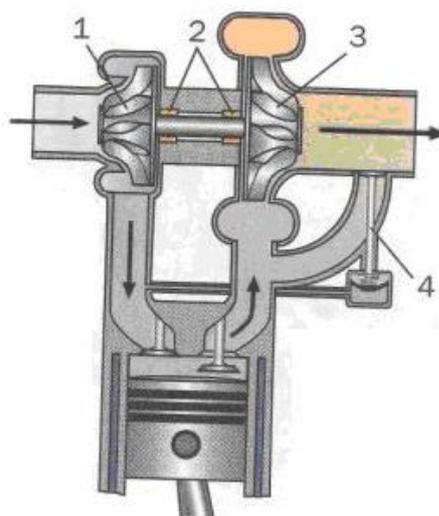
Регулирование наддува: 1 – колесо компрессора; 2 – подшипник ротора; 3 – колесо турбины; 4 – перепускной клапан
